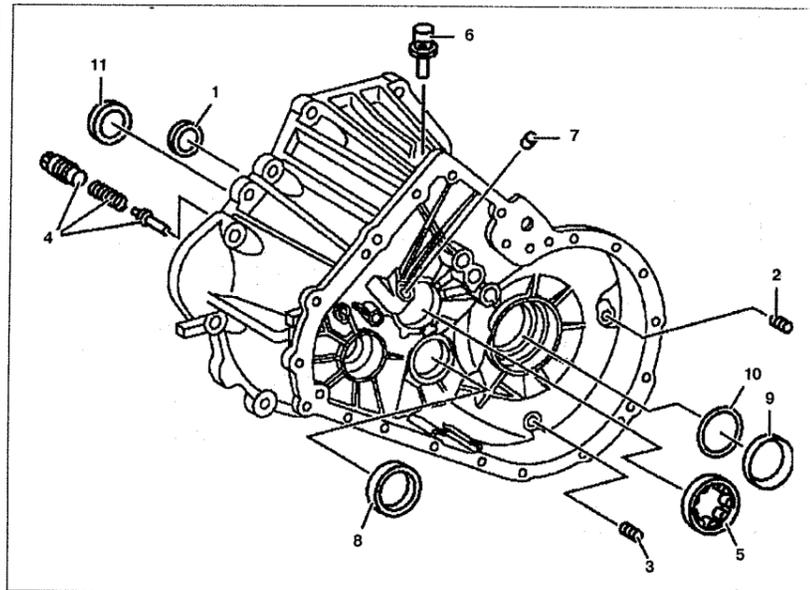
Корпус сцепления (автомобили с двигателями 611.980): 1, 11. Вращающийся сальник, 2. Маслозаливная пробка, 3. Маслозаливная пробка, 4. Блокировочное устройство шестерни заднего хода, 5. Роликовый подшипник ведущего вала, 6. Вентиляционный болт, 7. Втулка подшипника узла переключения передач, 8. Наружное кольцо роликового подшипника выходного вала, 9. Наружное кольцо конического роликового подшипника дифференциала, 10. Прокладка.
